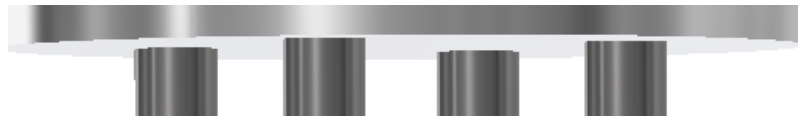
Captura de sección para análisis de soldadura de la pieza circular.
